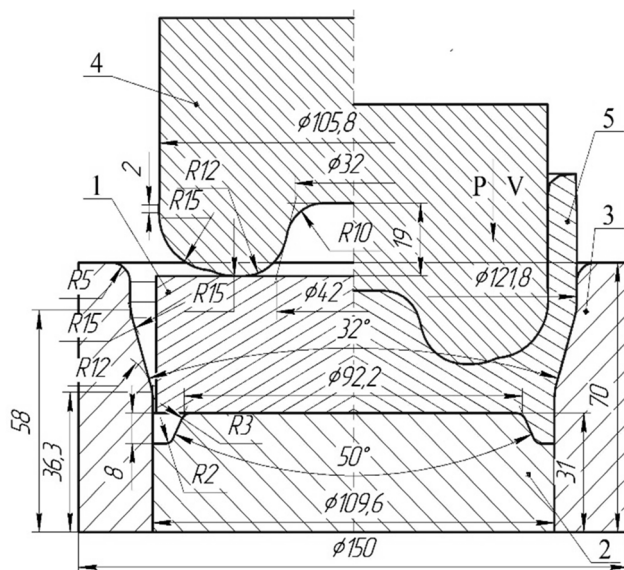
Схема зворотного видавлювання: 1 – заготовка; 2 – плита; 3 – матриця; 4 – пуансон; 5 – виріб
